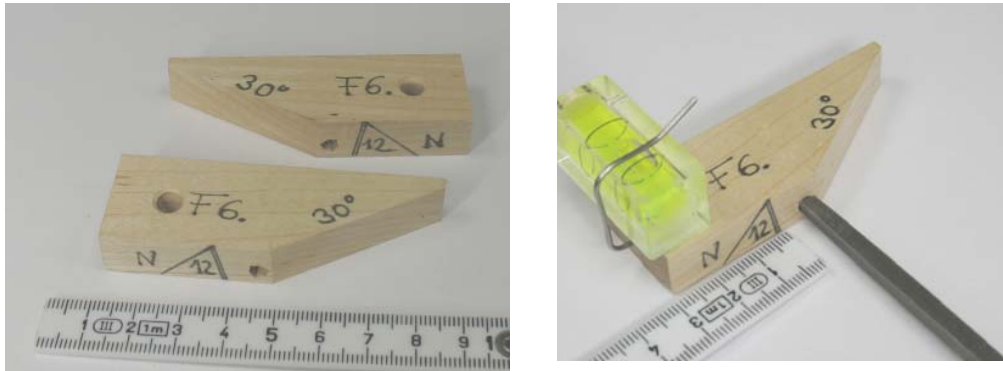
Winkellehre für Qs (Querschnitt) - bezeichnungen
